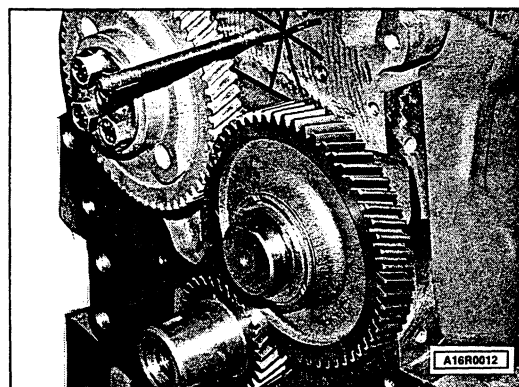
Referencias insertadas en los engranajes de la distribución para la puesta en fase del motor.
